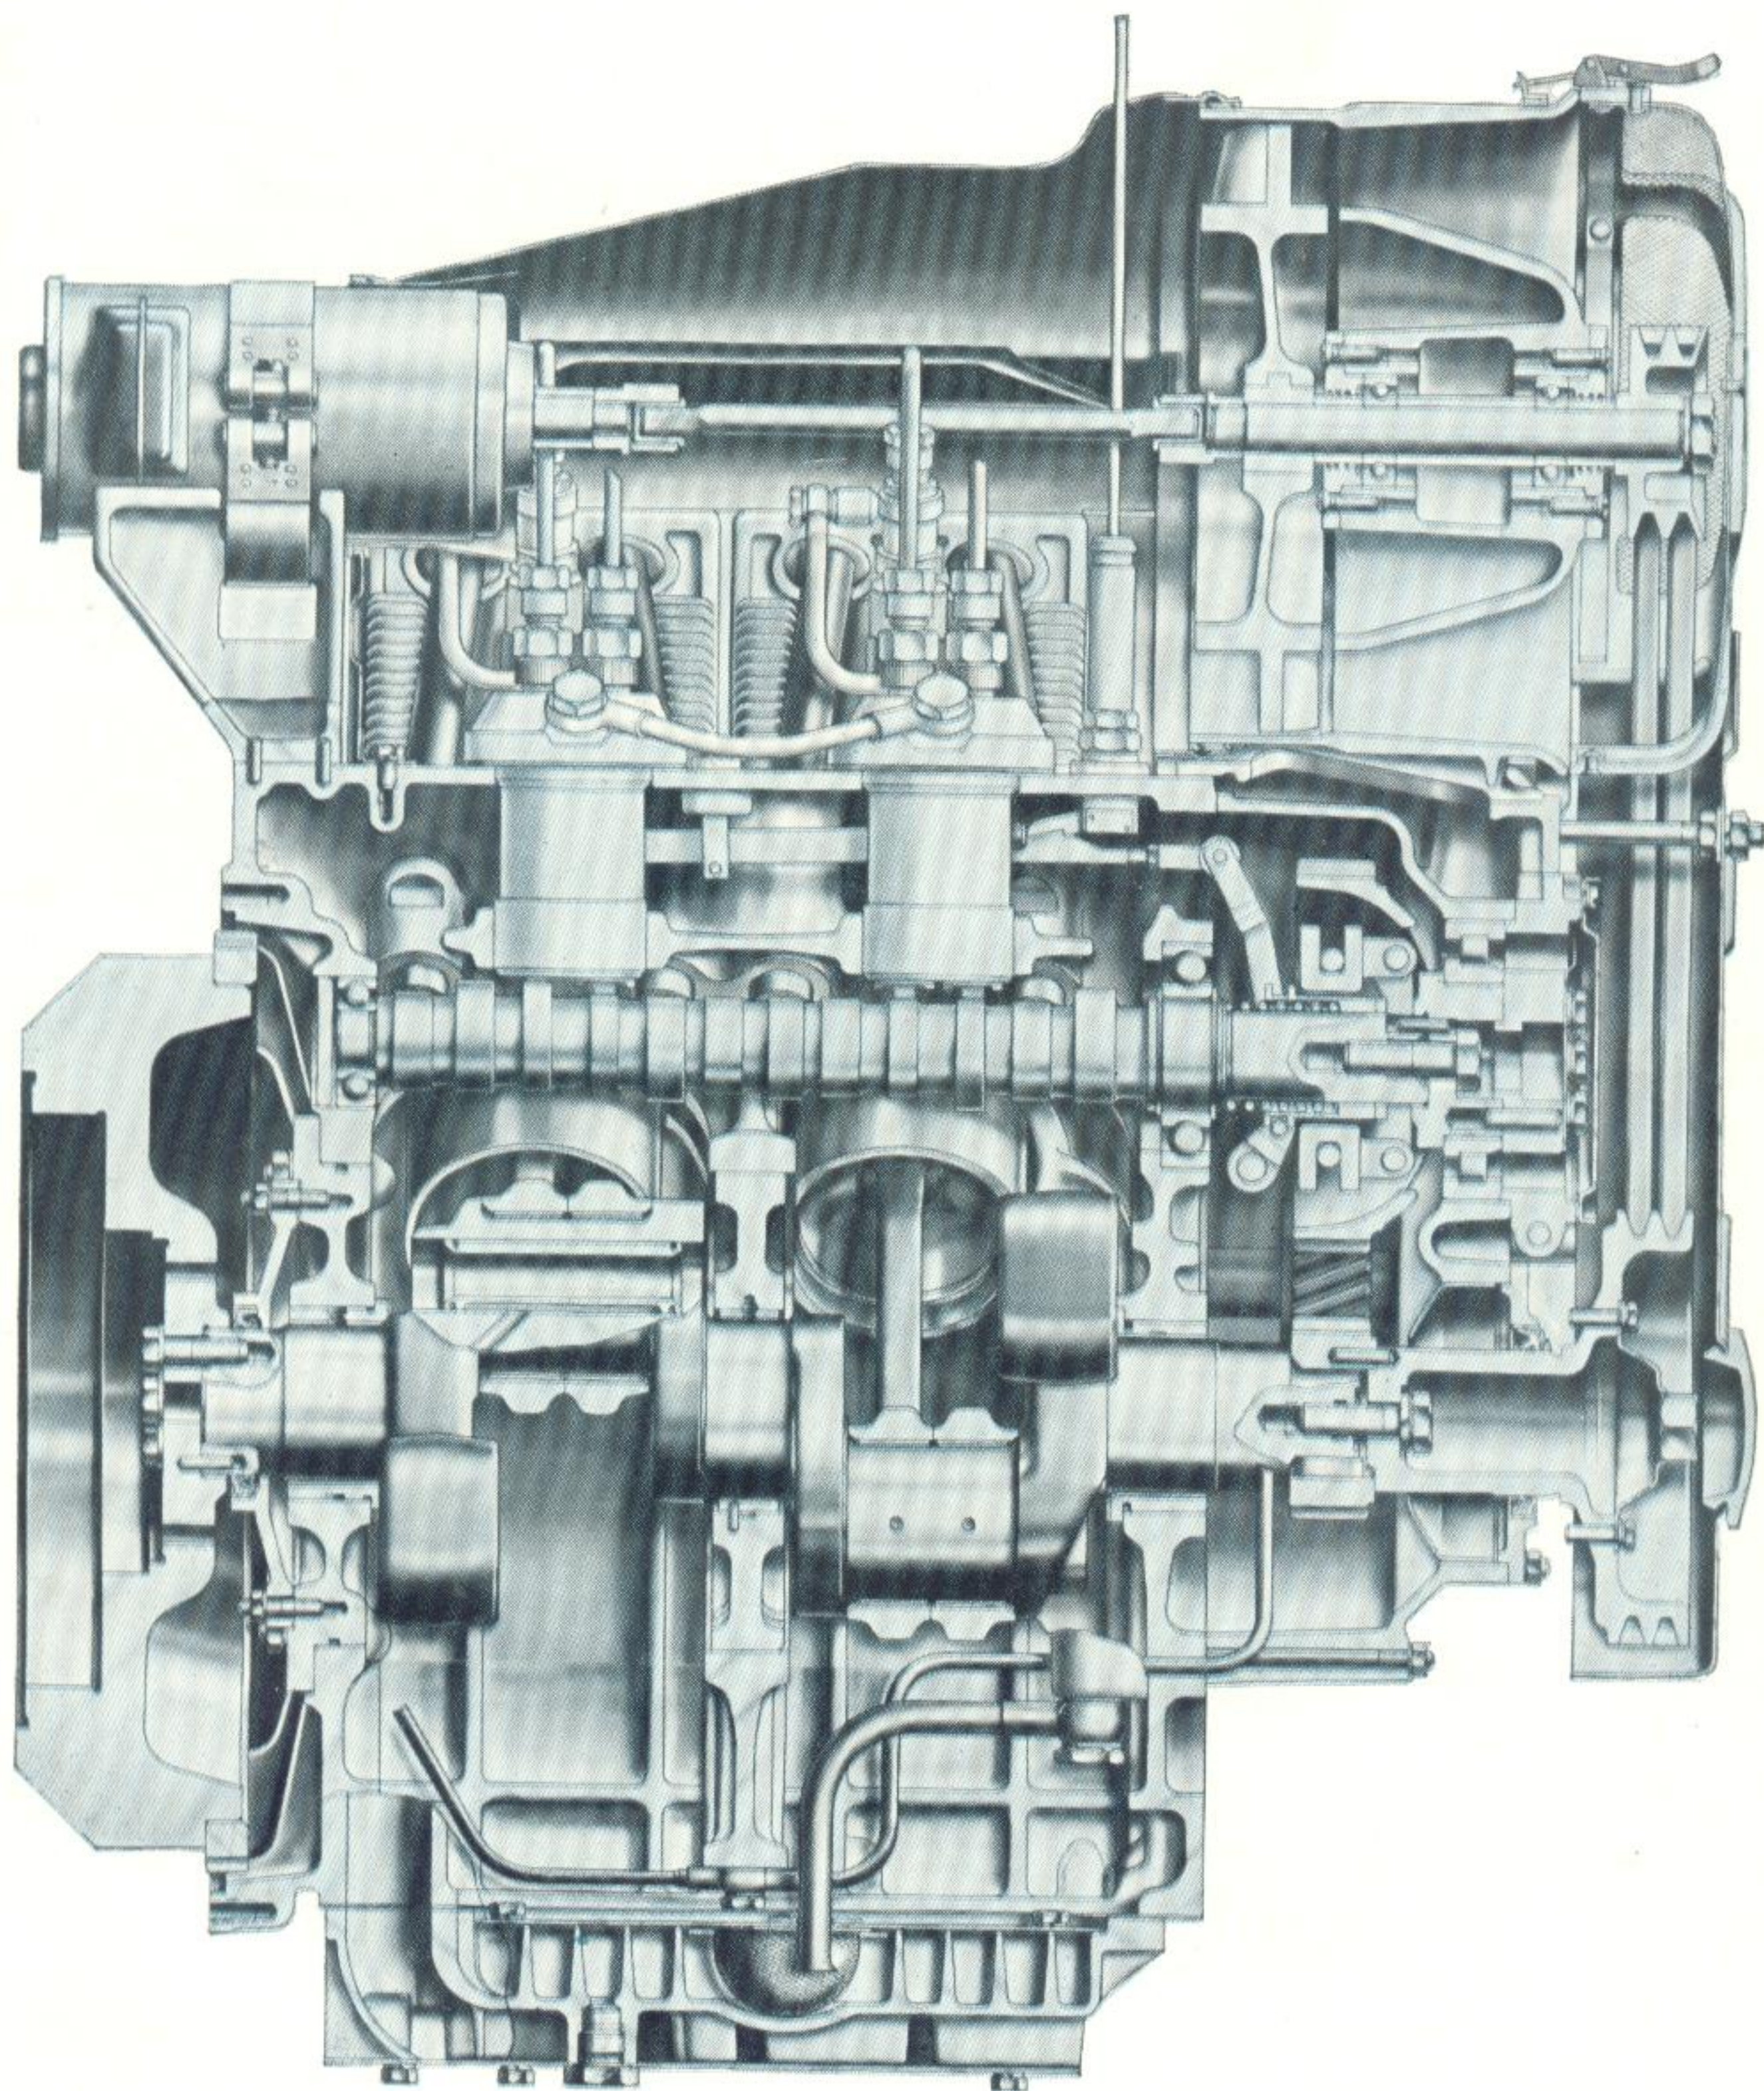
Motor 2 KVD 8 SVL, podélný řez
